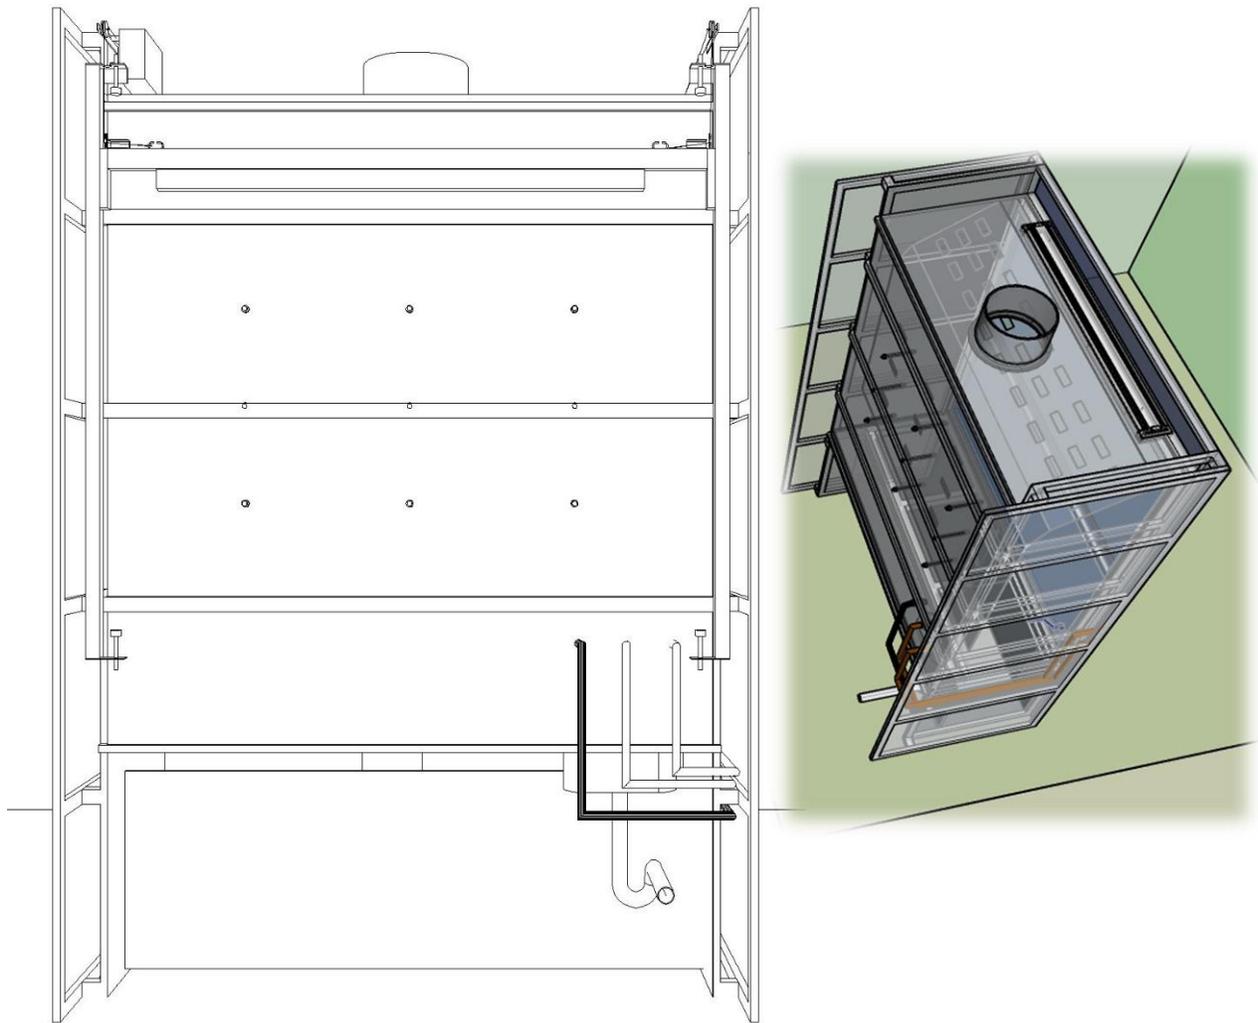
Campana de extracción VAV modelo 1 800. Vista con dimensiones en altura y ancho en plano sección.
